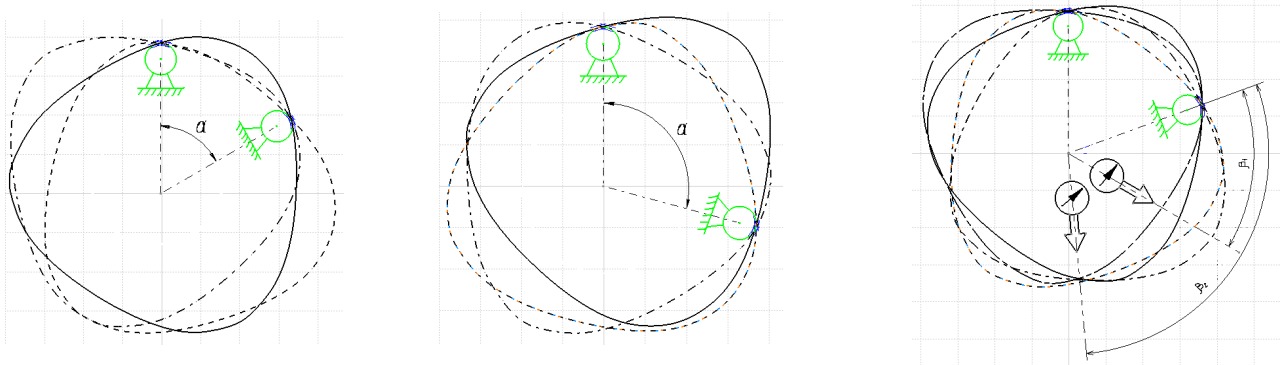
Вплив положення базових опор та датчика на базування вимірювальної поверхні
